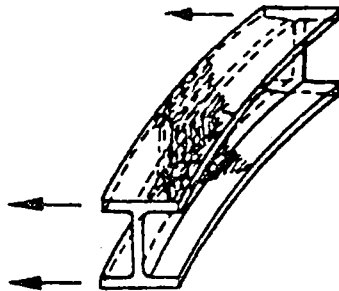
T profiline ısı kaması ve ısı yolunun uygulanması
